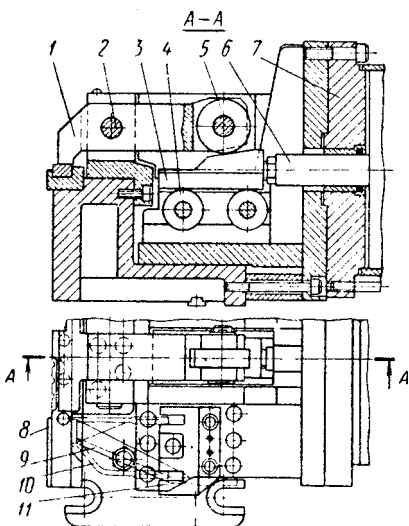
Приспособление для крепления вилок при протягивании гнезд в планках
